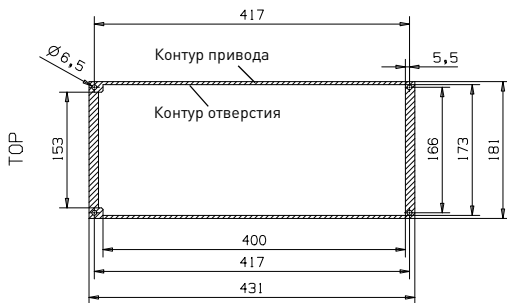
Размеры выреза для фланцевого крепления приводов типоразмеров MI5 (ед. изм.: мм)
